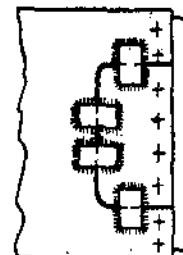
Вваренная в корпус котла заплата приклепана с одной стороны. Сварной шов усилен короткими наладками.
